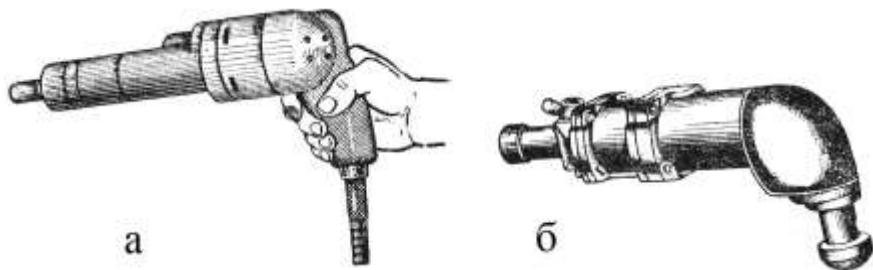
а – електрогайкокрут, б – пневматичний реверсний гайковерт
